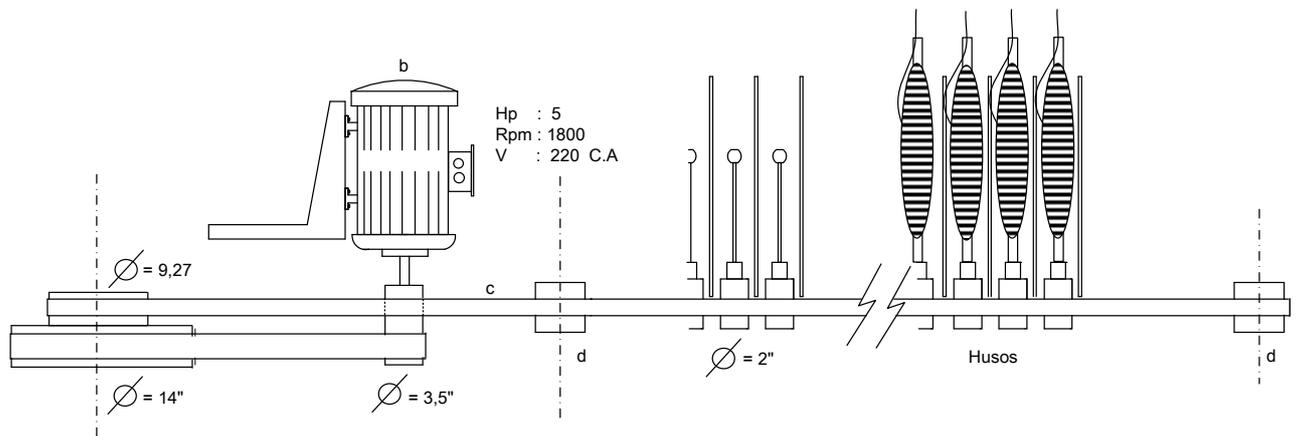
Movimiento de husos parte inferior con motor de 5 Hp
